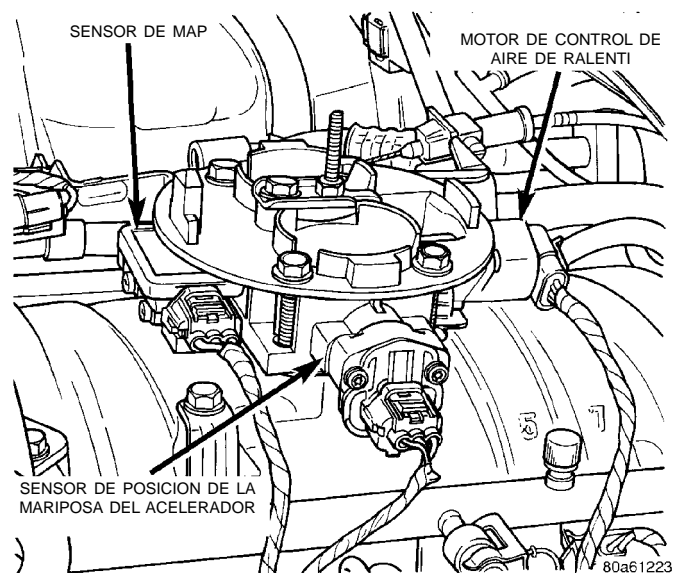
Localización del sensor y motor de IAC—Motores de 5.2L/5.9L
